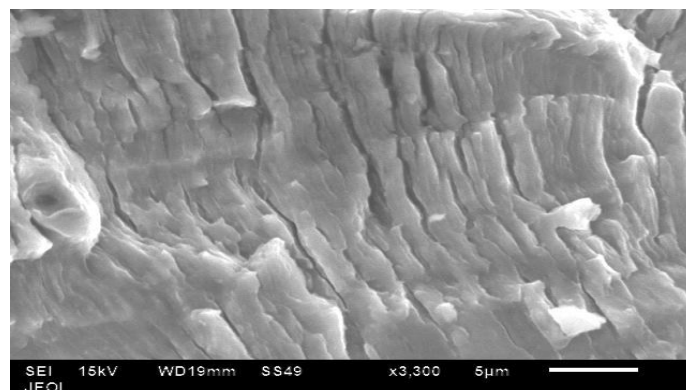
Analyse fractographique à 4mm de l'entaille pour une éprouvette non réparée sous H-L blocs à 1x 20
